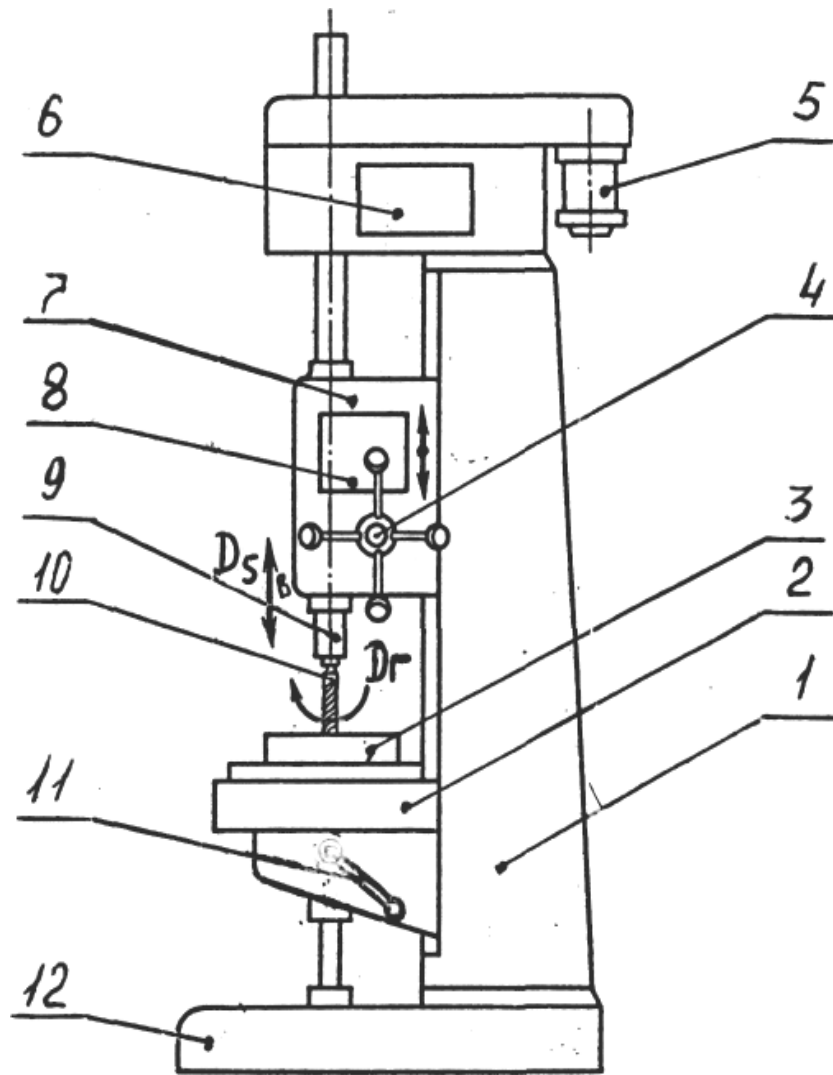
Общий вид вертикально-сверлильного станка:
